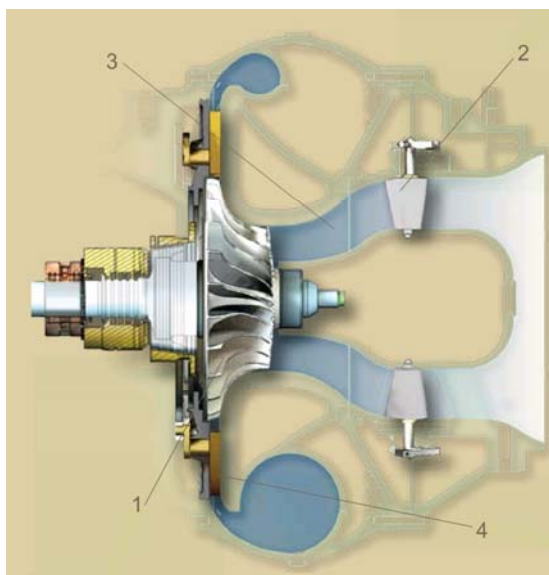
Современный вид воздушного центробежного компрессора: 1 – осерадиальное колесо; 2 – направляющий лопаточный аппарат; 3 – кольцевой подводящий канал; 4 – лопаточный диффузор
